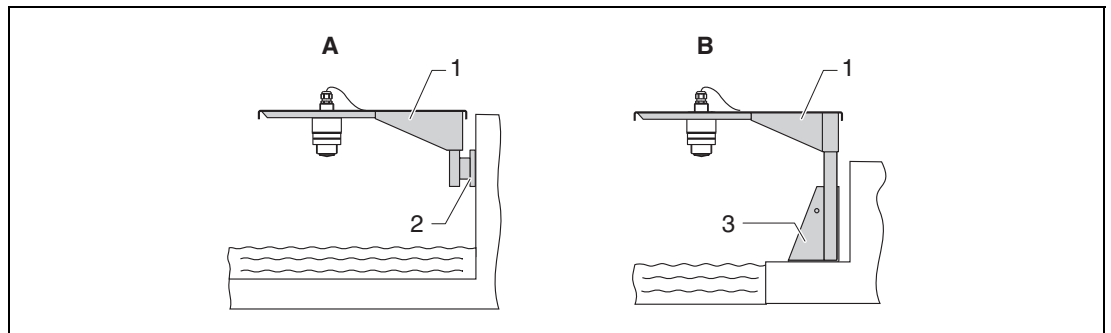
Montageart Sensor Prozessanschluss Rückseite
